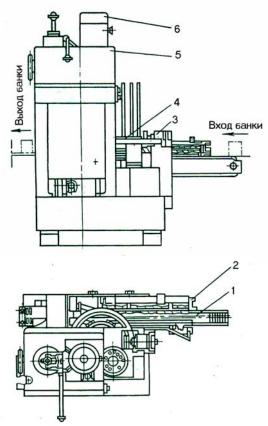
Закаточная машина Б4-КЗТ-11М: 1 — транспортер; 2 — шнек; 3 — маркирователь; 4 — магазин крышек; 5 — коробка скоростей; 6 — электродвигатель
